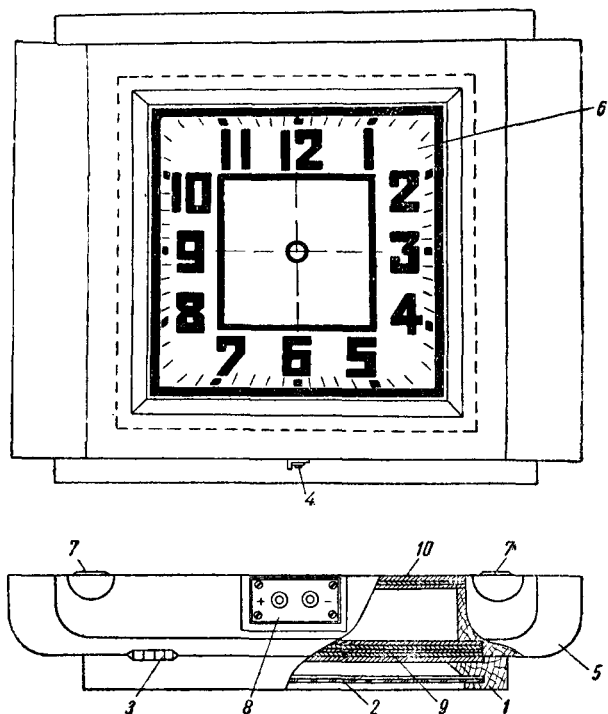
Деревянный корпус вторичных часов ЭВЧД-20.
